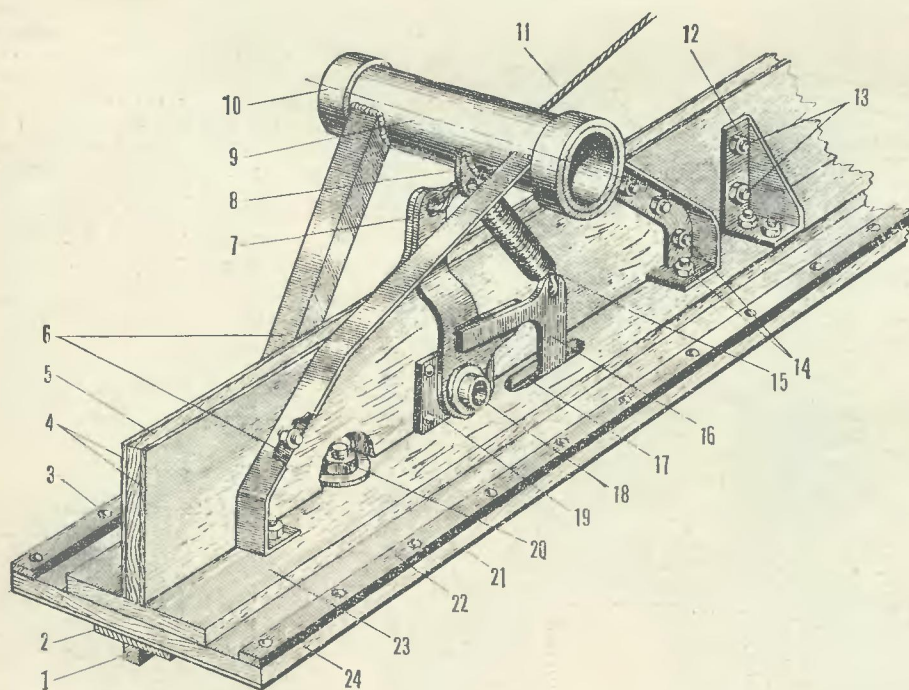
Лыжа и ее тормозное устройство: 1 — подрез, 2 — лента подреза, 3 — стяжные заклепки, 4 — фанерная обшивка лонжерона, 5 — лонжерон, 6 — стойки кабана, 7 — рычаг тормоза, 8 — ушко пружины, 9 — втулка кабачника, 10 — усиливающий обод втулки, 11 — трос тормоза, 12 — угольник крепления лонжерона, 13, 14 — болтовое крепление, 15 — обратная пружина тормоза, 16 — тормоз, 17 — окно тормозного рычага, 18 — ось тормозного рычага, 19 — усиливающая накладка, 20 — болтовое крепление подреза, 21 — подошва лыжи (стальная), 22 — лента крепления подошвы, 23 — усиливающие продольные подкладки подошвы, 24 — подошва лыжи (фанерная).
